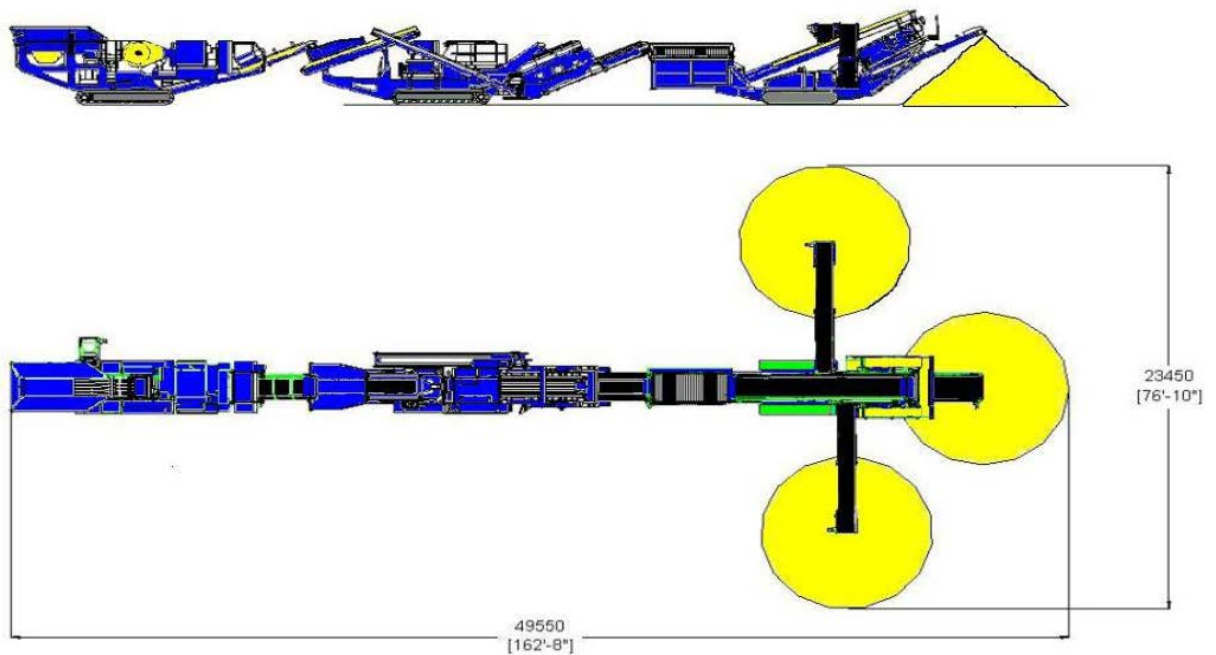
загальний вигляд компоновки обладнання установки фірми FINTEC.
